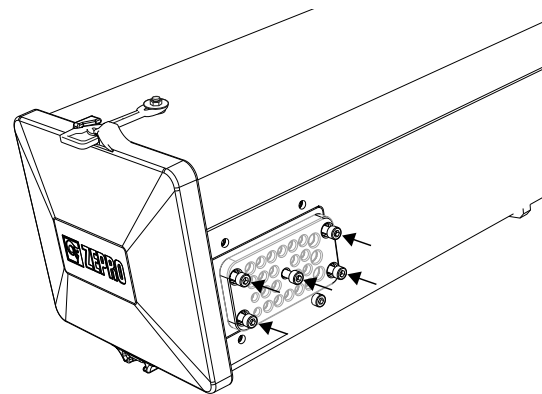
Die fünf Schrauben der Kabeldurchführung
